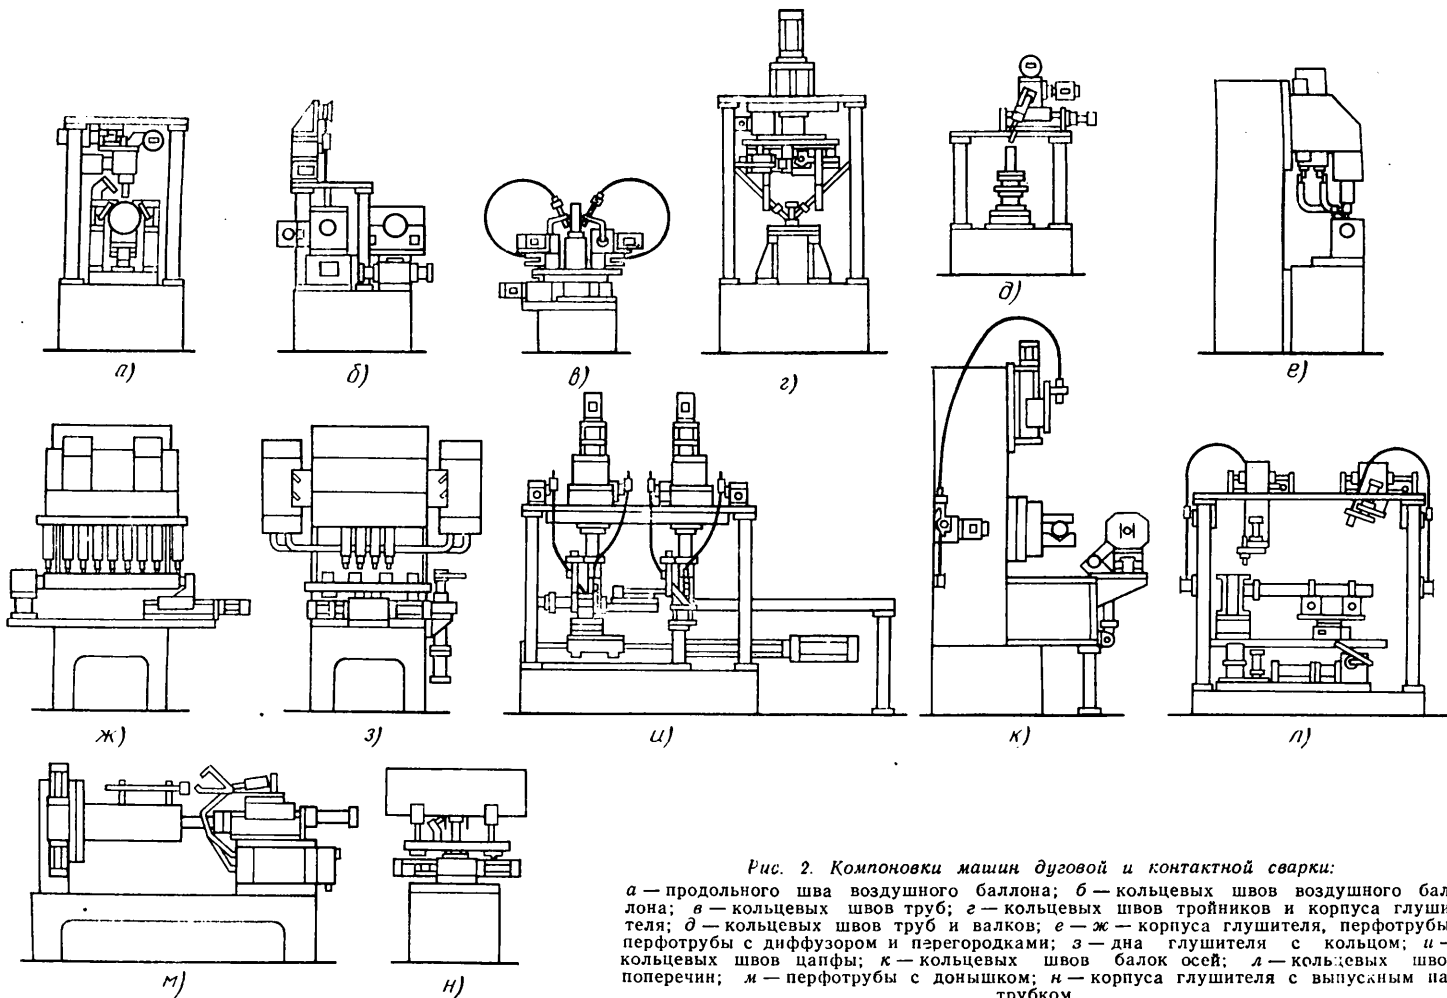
Компоненты машин дуговой и контактной сварки:
